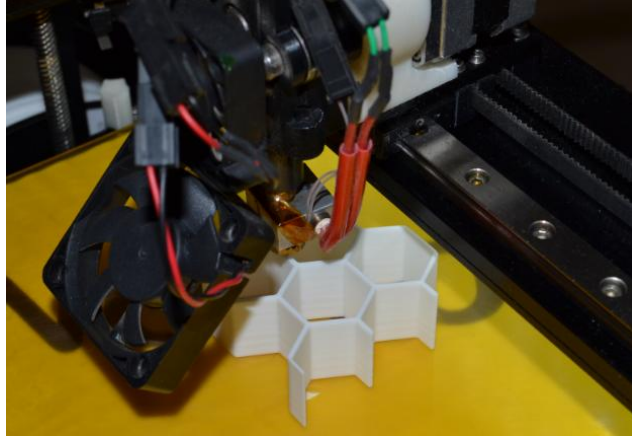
Εκτυπωτής τύπου M2 της Maker Gear.
